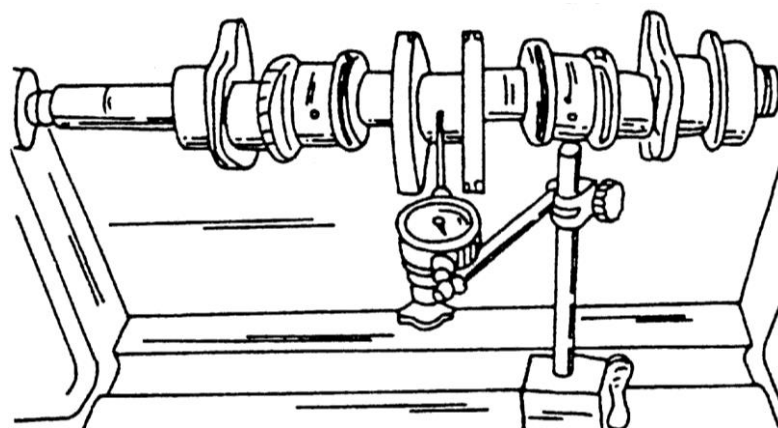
Вимірювання величини биття колінчастого вала
